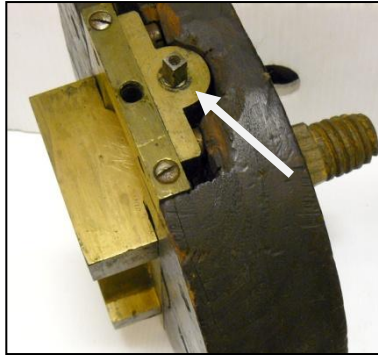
Chuck med justerskrue (se pil), fra "rose engine lathe" Blythe House
